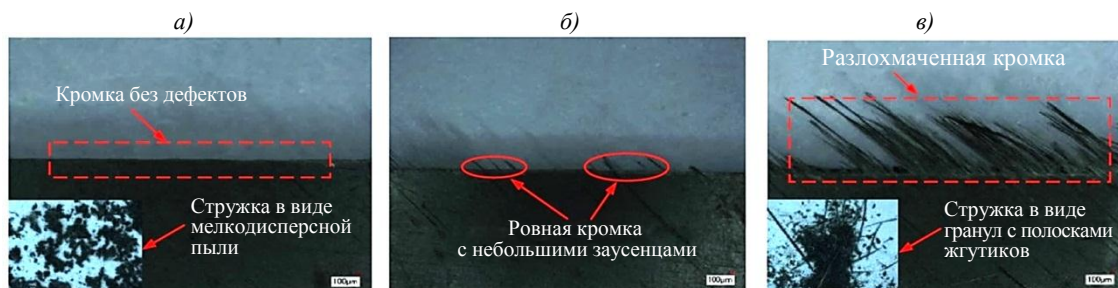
Дефекты кромки углепластика на длине фрезерования 12 (а), 42 (б) и 72 м (в)
